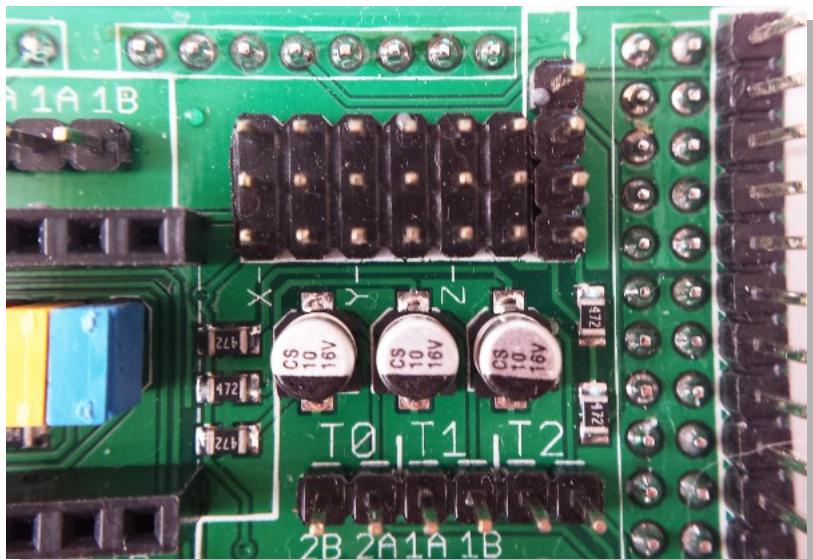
soudure sur endstop monté sur carte makerbot
